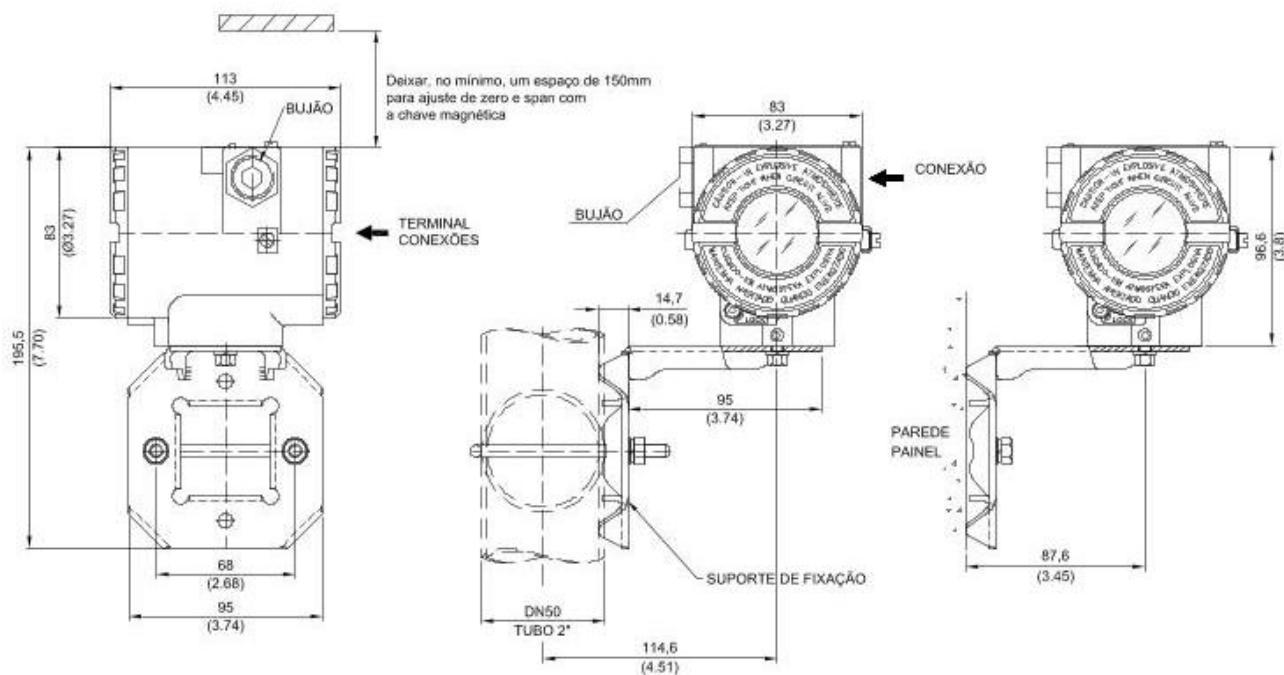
Desenho Dimensional e Posições de Montagem
